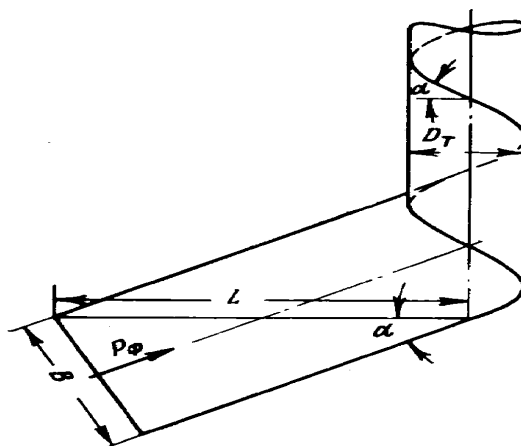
Схема формовки трубной заготовки при спиральной сварке трубы
